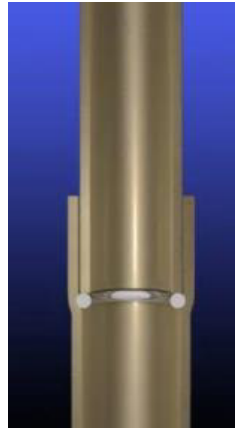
Anillo interior para el diseño de las juntas soldadas.
